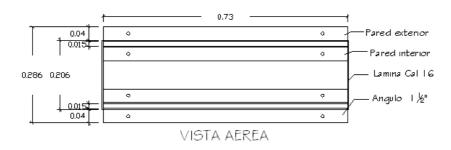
Ingeniería de detalle del molde empleado para la construcción de paneles tierra-concreto
